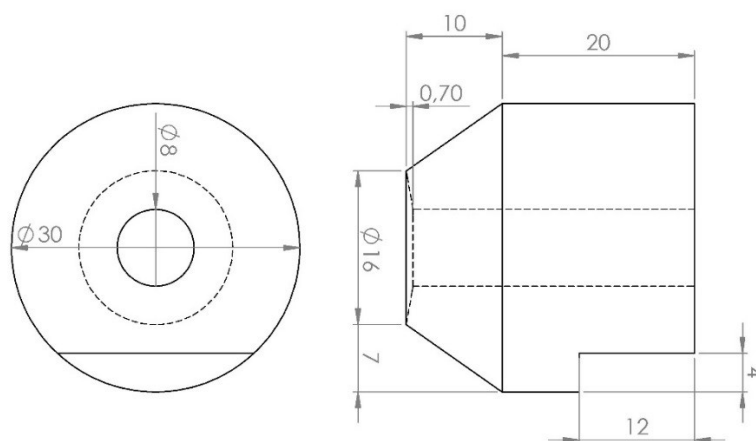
Desenho técnico do *shoulder* de alumina para a ferramenta da AT2.
